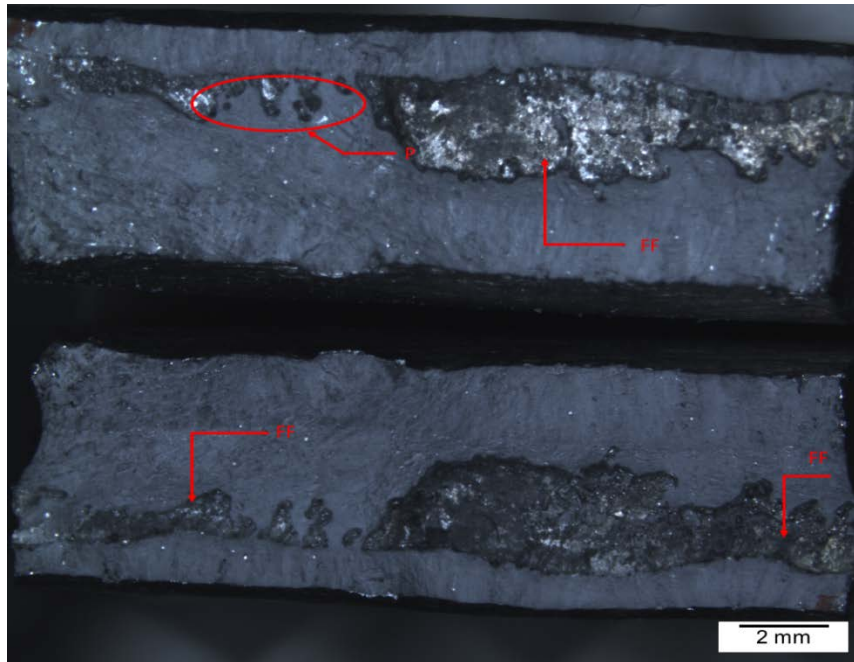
Imagen por estereoscopio de la fractura del ensayo de tensión T2 unión soldada ER-308L.
